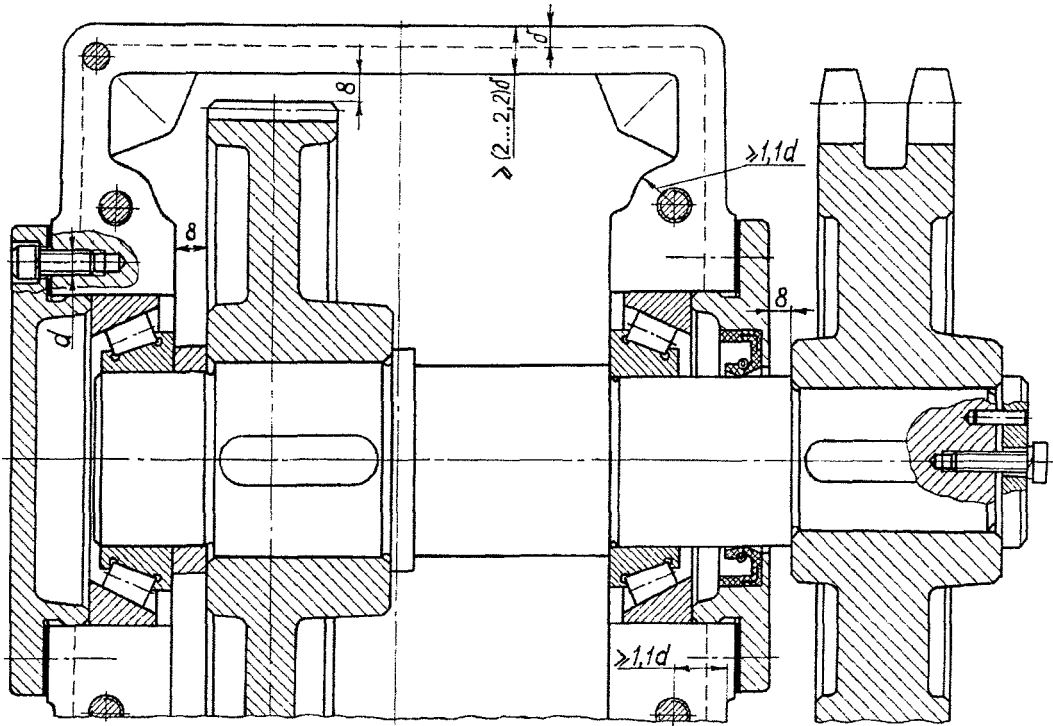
Вариант конструкции тихоходного вала двухступенчатого цилиндрического редуктора, выполненного по простой развернутой схеме
